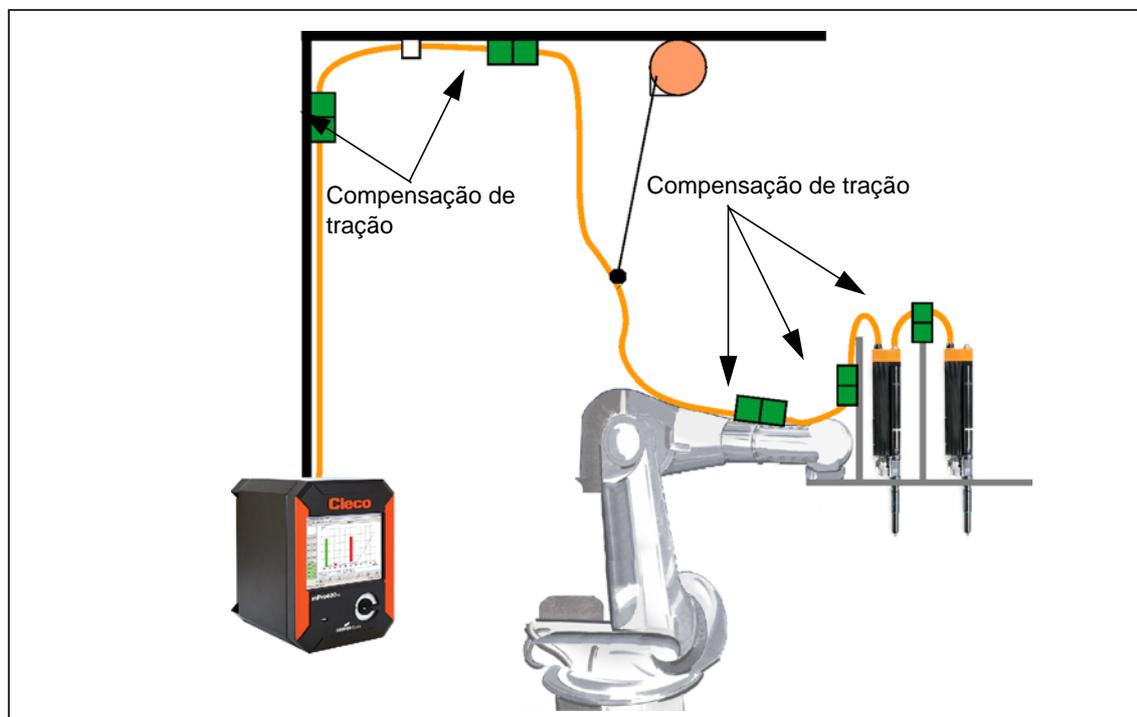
Aplicação com robô (exemplo, outras instalações possíveis)
